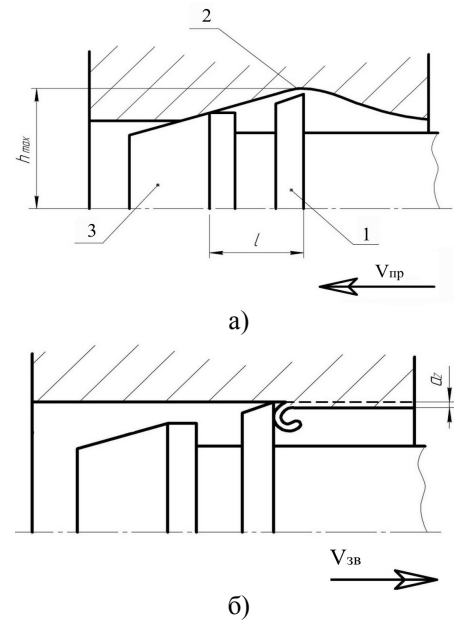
Схема роботи протяжки з розвернутим зубом: а) при прямому русі інструмента; б) при зворотному русі
